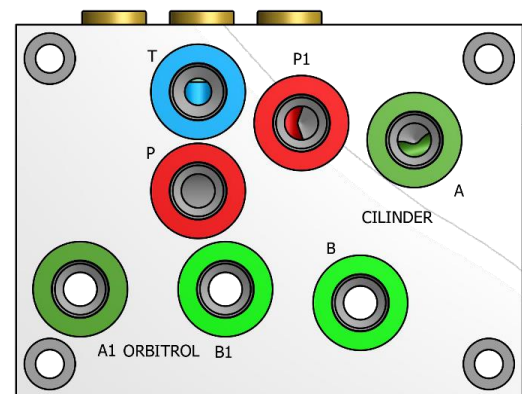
Anschlüsse für das hydraulische Open Center Manifold.
